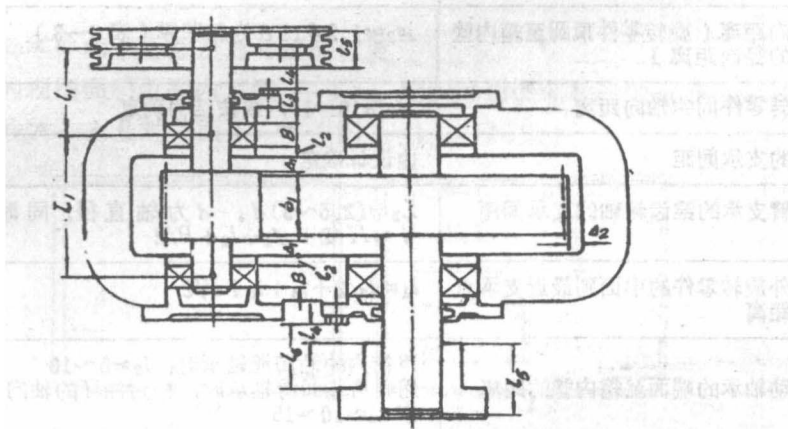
二级圆柱齿轮减速器零件的位置尺寸
